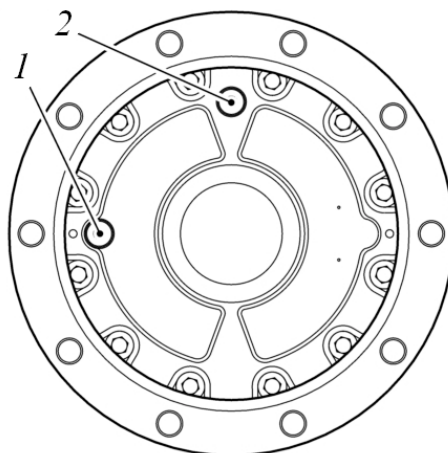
Процедура проверки уровня масла в бортовом редукторе
